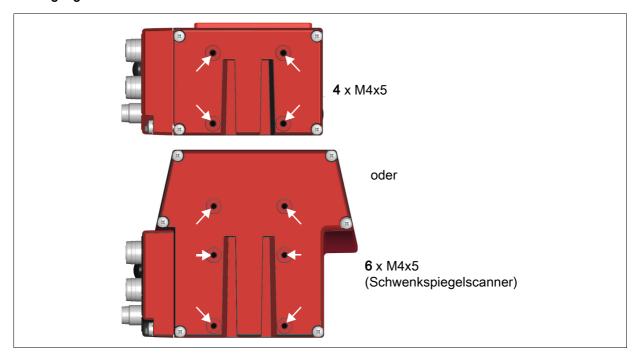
Befestigungsmöglichkeiten mittels M4x5 Gewindelöchern
